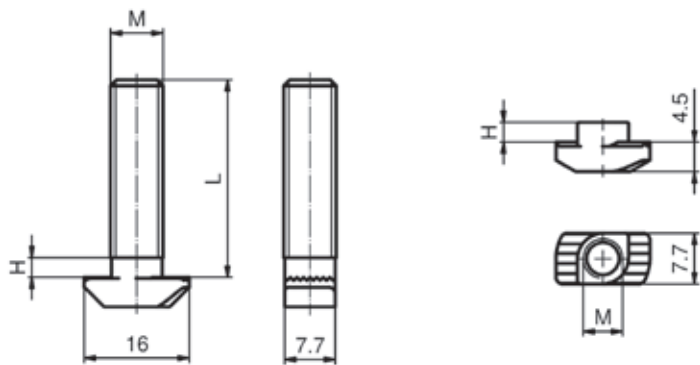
Abmessungen Hammerschrauben und Hammermuttern AXF
